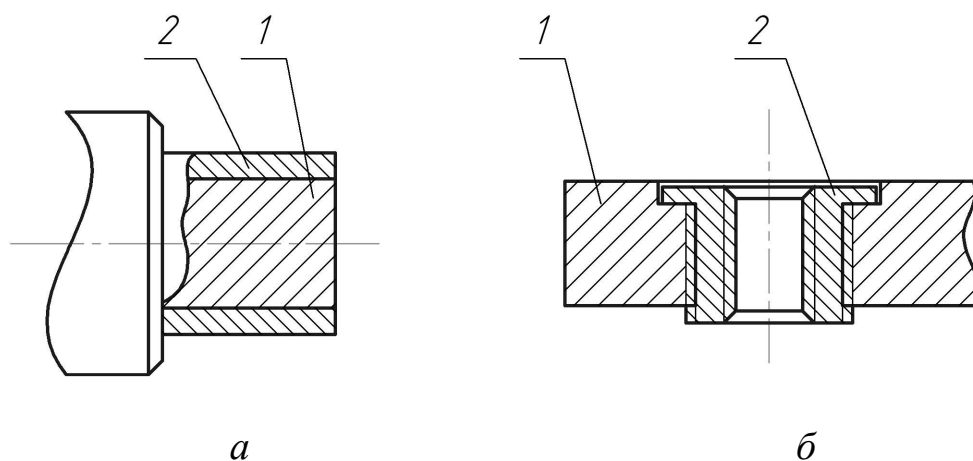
Восстановление изношенных шеек цапф (*а*), резьб (*б*) постановкой дополнительных деталей: *1* – изношенная деталь; *2* – дополнительная деталь
